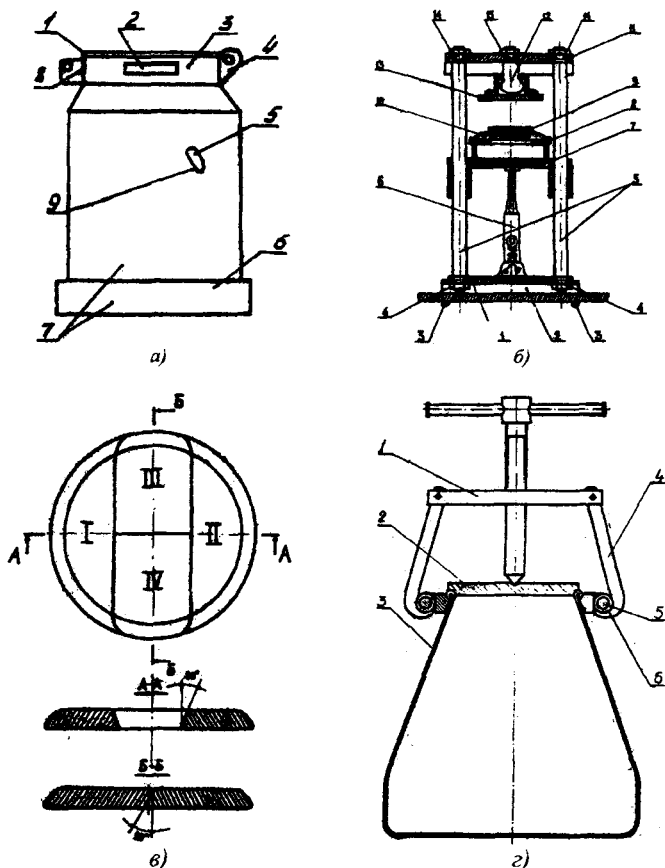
Дефекты и приспособления для ремонта доильных ведер:
